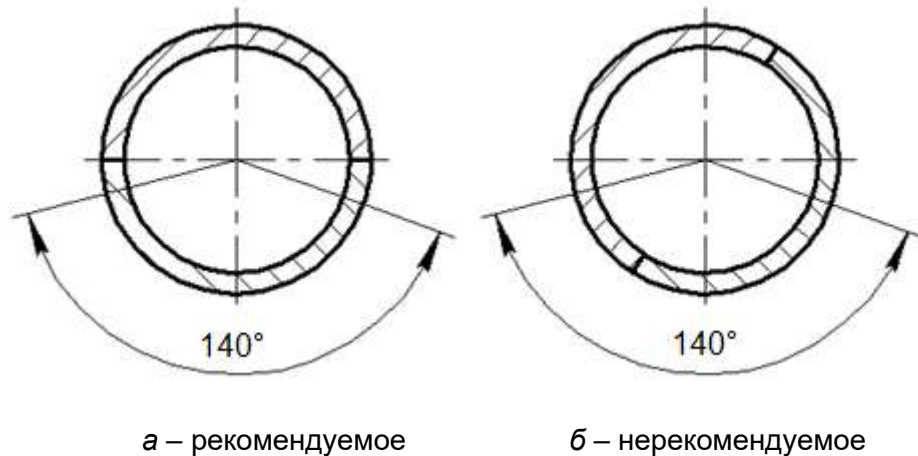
Расположение сварных швов в нижней части УТ
